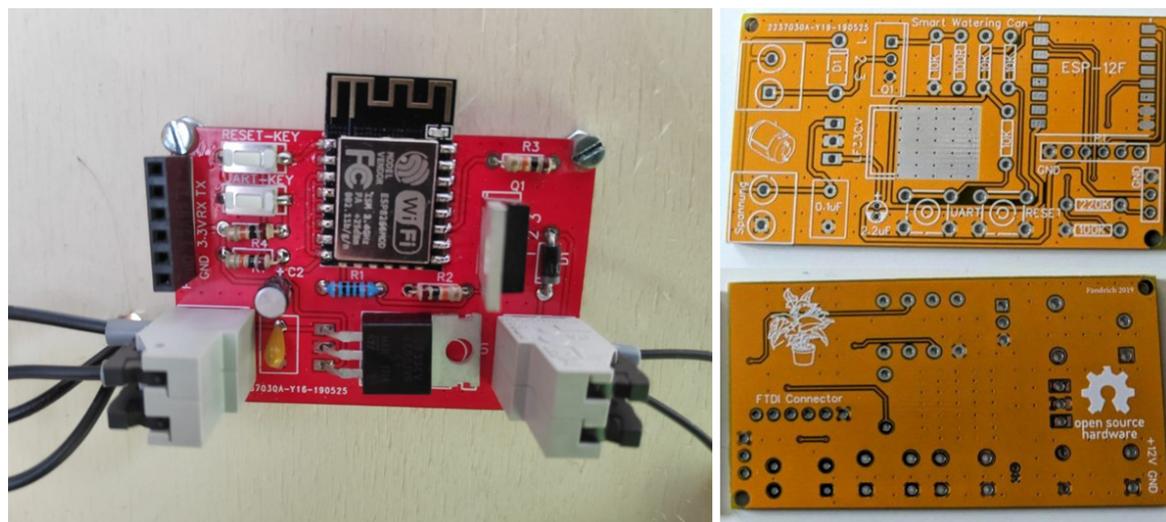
Für die Veranstaltung gefertigte Platinen. Links: PCB des Fütterungsautomaten. Rechts: Unbestückte PCB des Bewässerungssystems<sup>37</sup>
